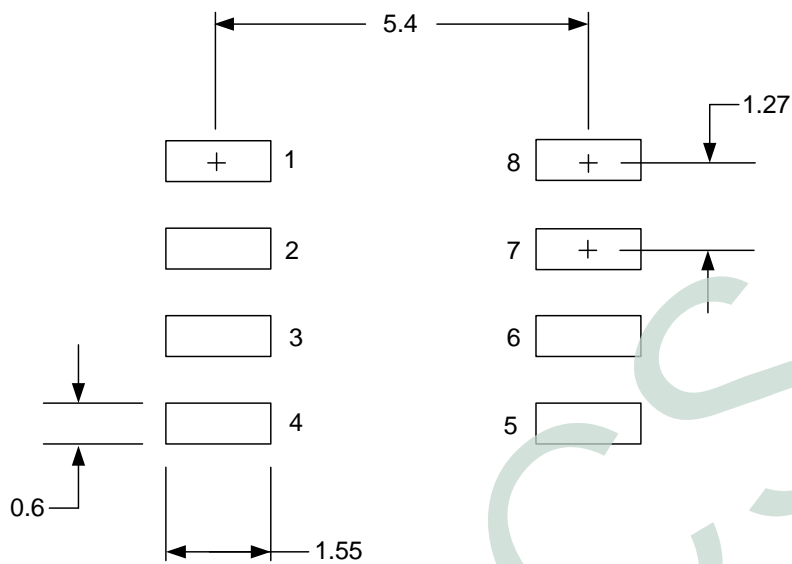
PCB 焊盘: 8-引脚 SOP
